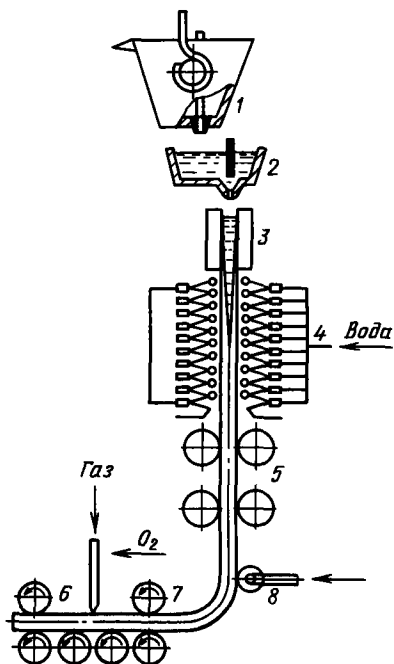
Схема установки непрерывного литья заготовок с использованием теплоты жидкой стали:
